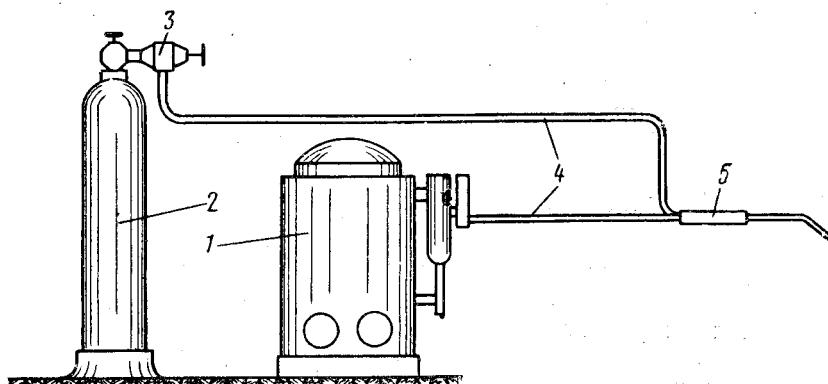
Схема установки для ацетилено-кислородной сварки и наплавки:
